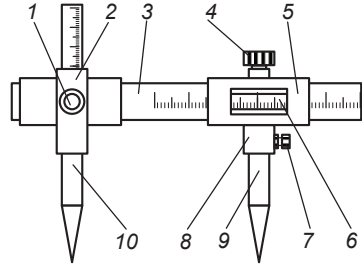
Штангенциркуль для разметки окружностей, больших диаметров
